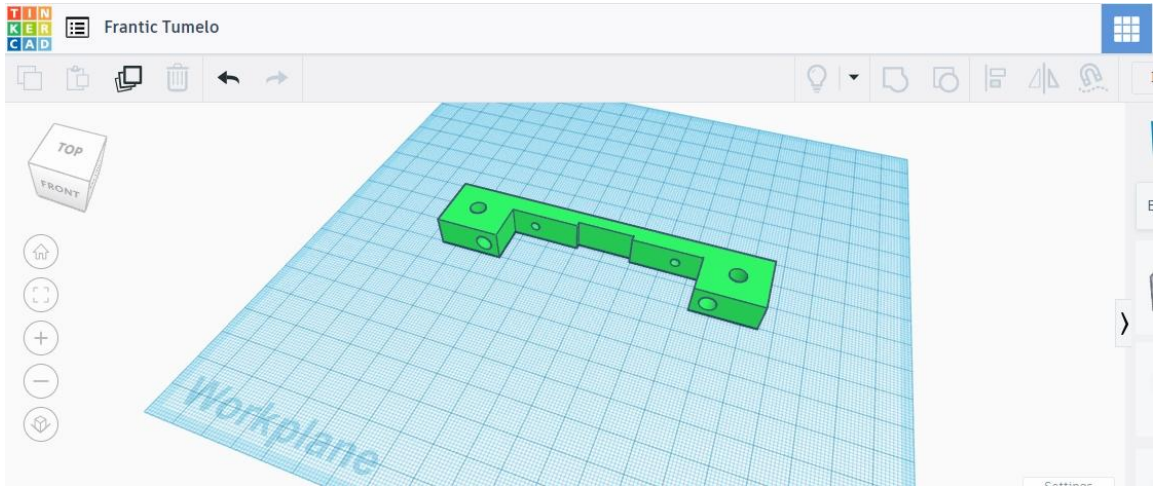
Зовнішній вигляд деталі Y1_CNC.
